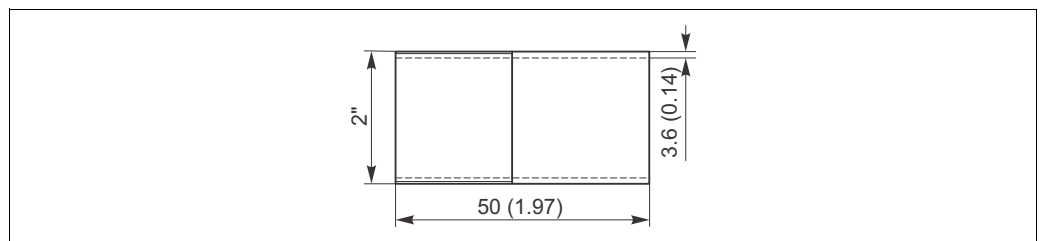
Einschweißnippel, Abmessungen in mm (inch)
